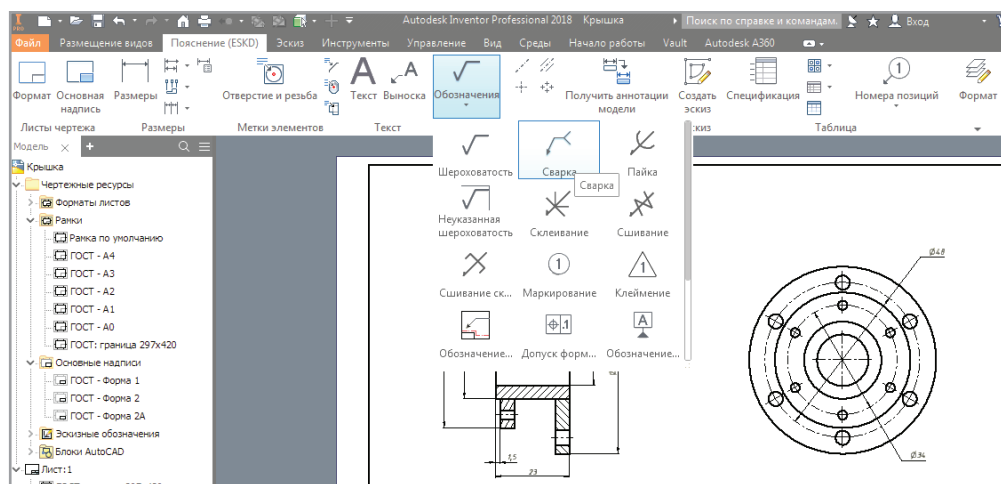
Обозначение сварных швов на чертеже
